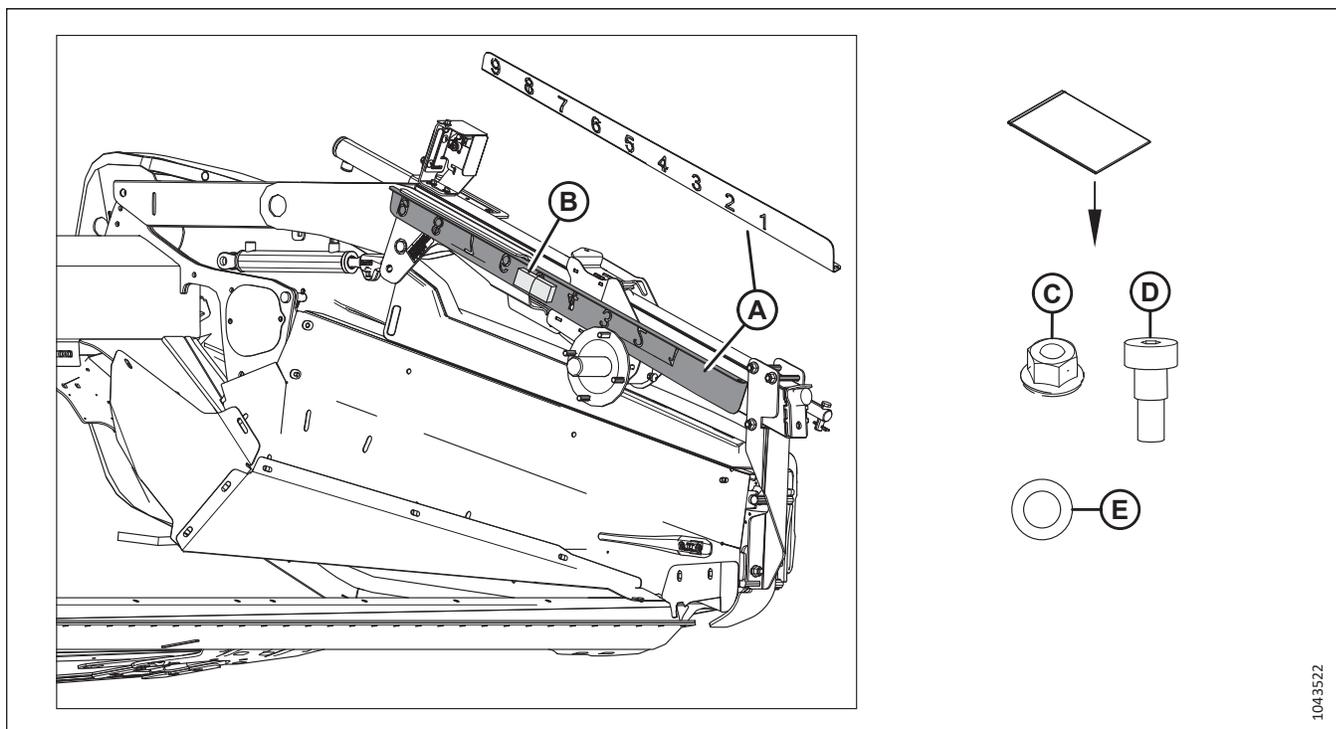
Emplacement d'expédition de l'indicateur avant-arrière, sac de pièces MD N° 368002
